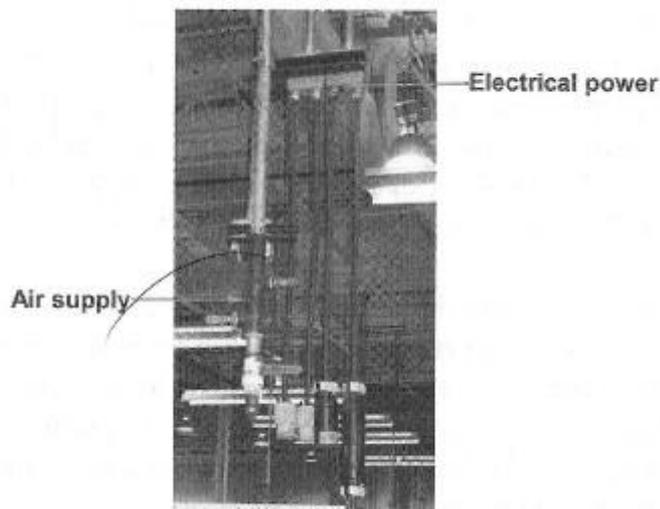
Impiantistica disponibile dalla rete soprastante lo stabilimento.
